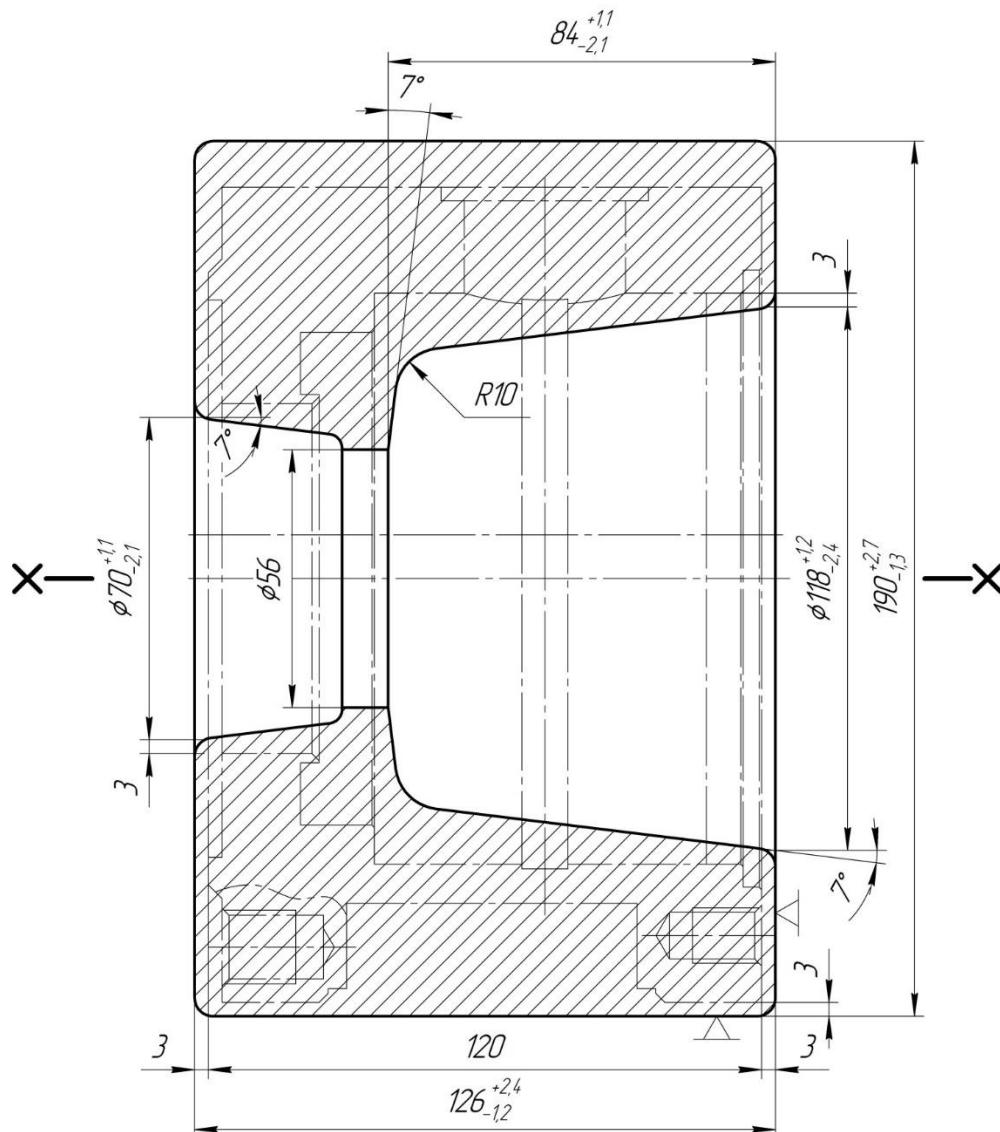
Креслення заготовки корпусу штампованиого на КГШП
